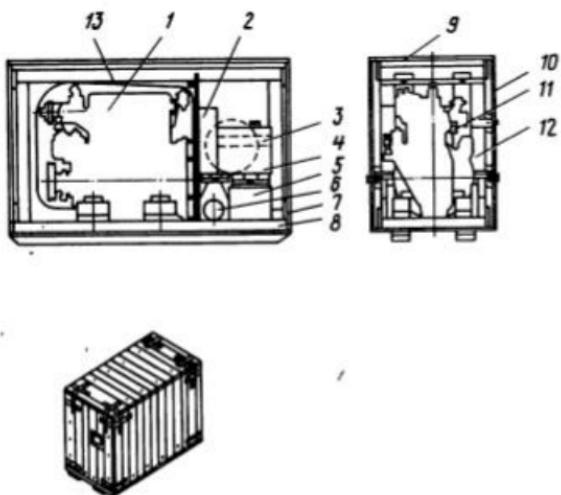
Упаковка дизеля 4ч 8,5/11:
